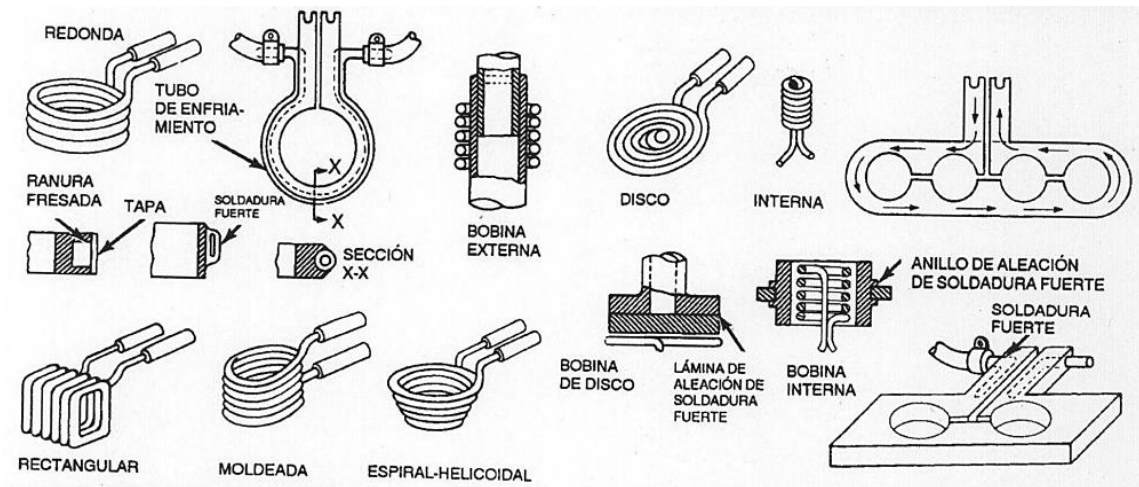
5 Bobinas y placas típicas de la soldadura brazing por resistencia. (11)
